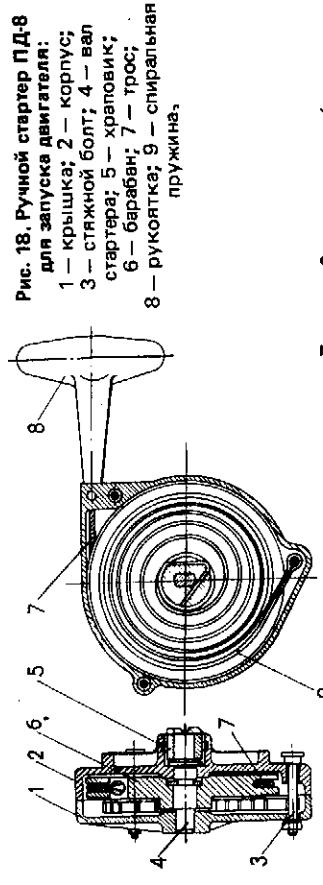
Ручной стартер ПД-8 для запуска двигателя:
